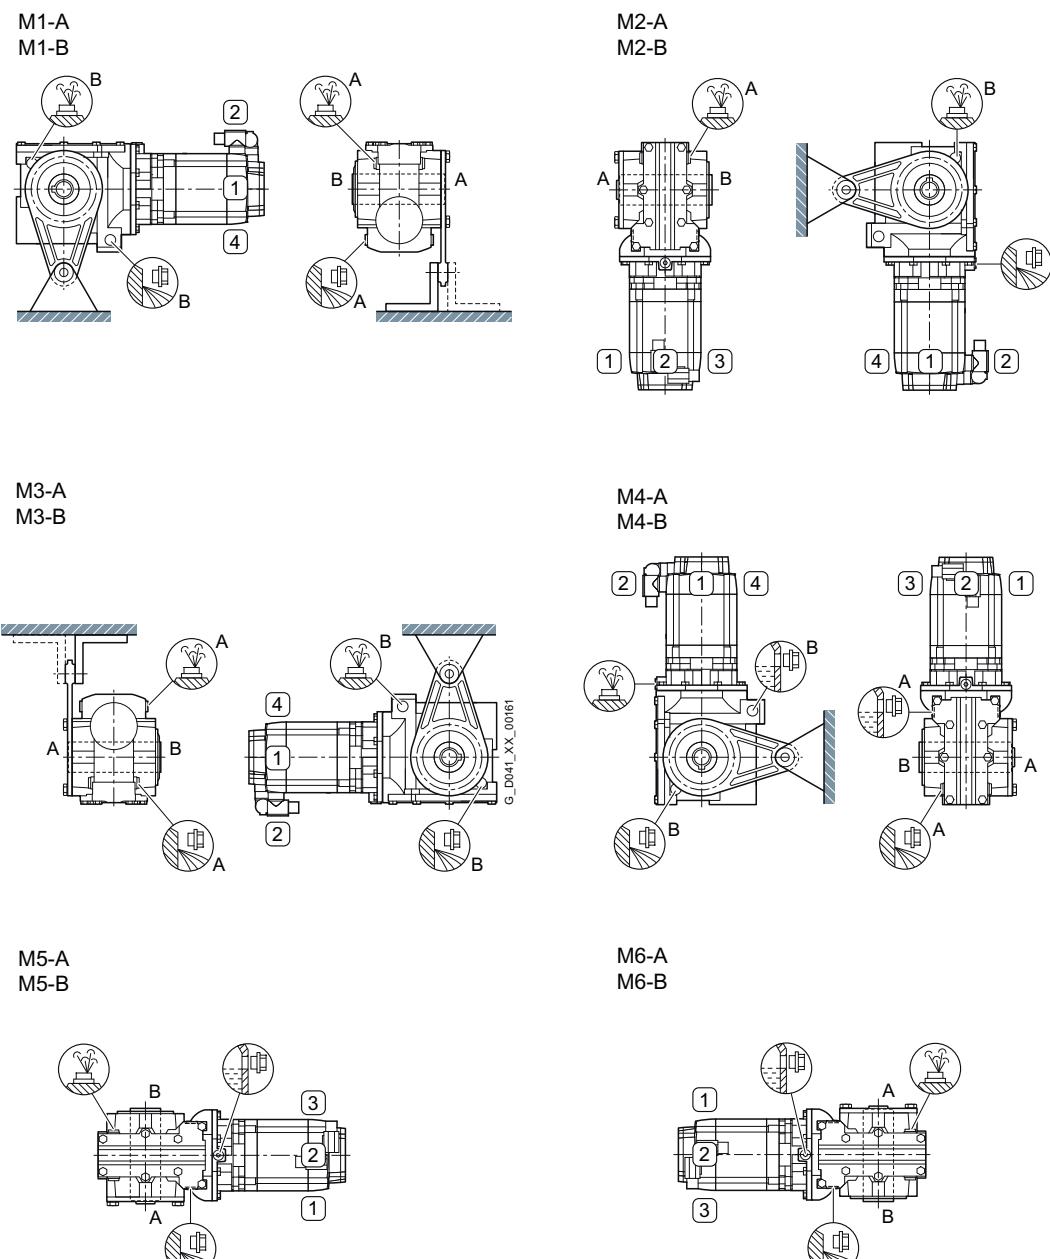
Einbaulagen für Servo-Stirnrad-Schneckengetriebemotor CAD, Aufsteckausführung, Baugrößen 29, 2-stufig
